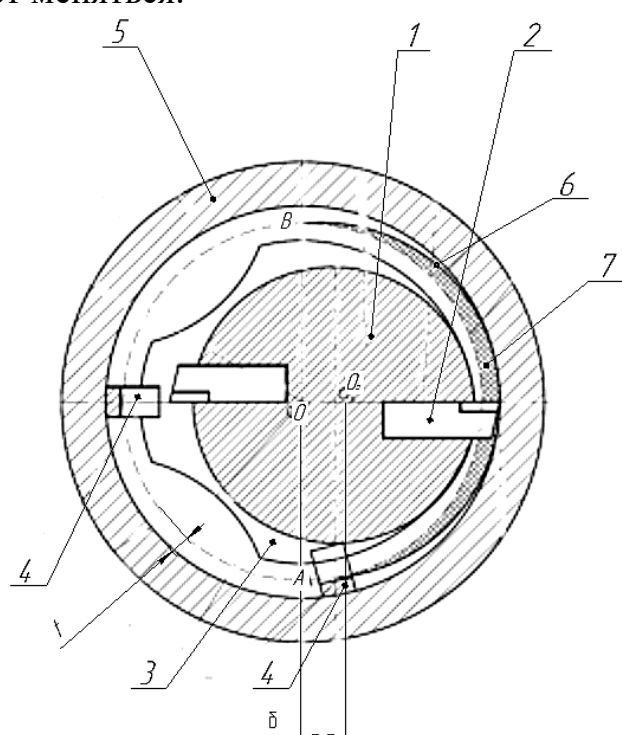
Обработка отверстий скоростным фрезорастачиванием
